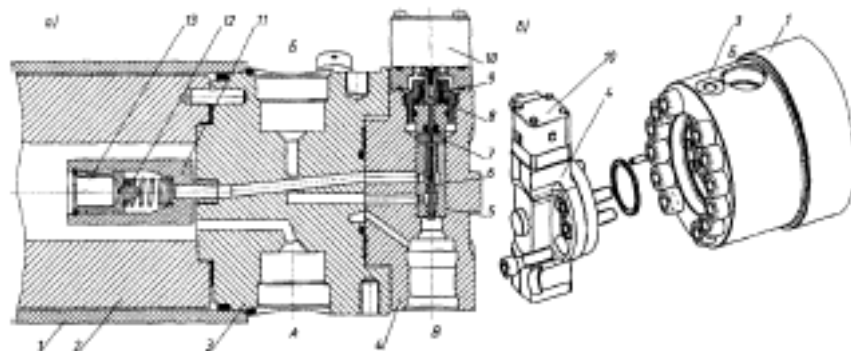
Блок управління подачею палива двигунів фірми MAN: 1 - захисний кожух акумулятора; 2 - корпус акумулятора; 3 - торцева кришка; 4 - блок клапанів управління паливоподачею; 5 - втулка головного клапана управління паливоподачею; 6 - головний клапан управління паливоподачею; 7 - сідло кулькового пускового клапана; 8 - притискний шток пускового клапана; 9 - притискна пружина; 10 - соленоїд; 11 - гідравлічний циліндр клапана-обмежувача максимальної подачі палива; 12 - запірний конус клапана-обмежувача; 13 - гідравлічний поршень клапана-обмежувача.
